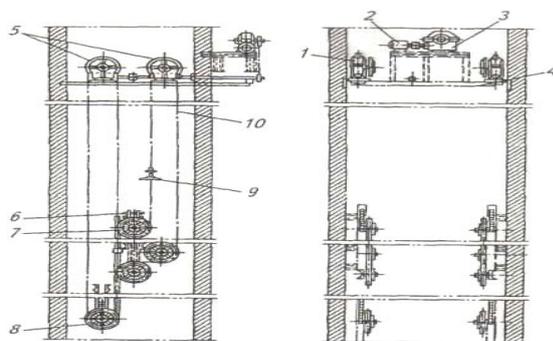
Малая автокоптилка АМ-360: 1, 3 - редукторы; 2- электродвигатель; 4 - цепная передача; 5, 7, 8 - звездочки; 6 - натяжная станция; 9 - траверсы; 10 - цепи.
